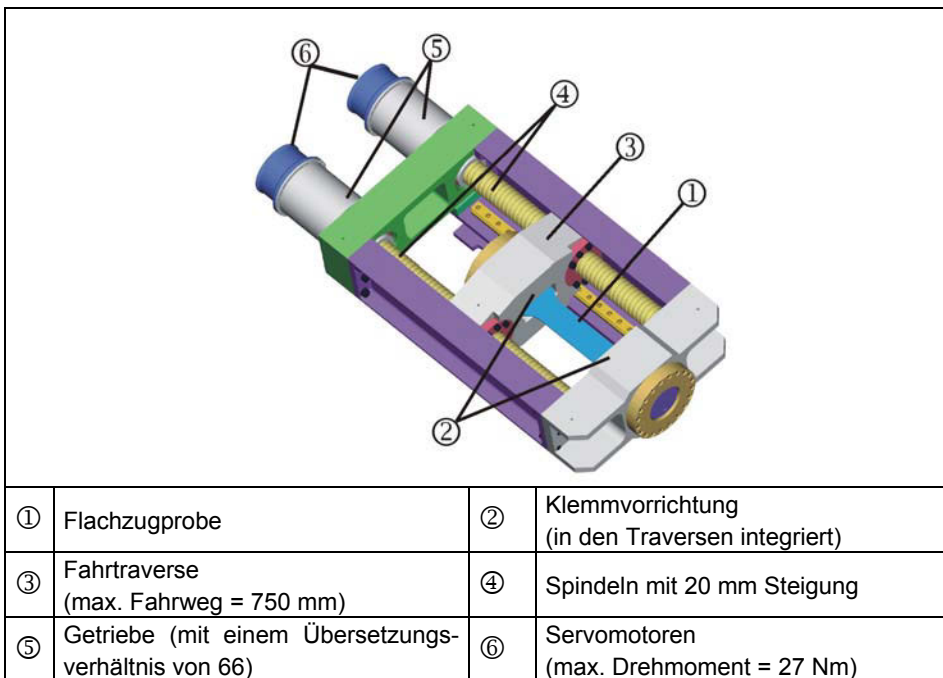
Komponenten des Controlled Tensile Weldability - Tests
